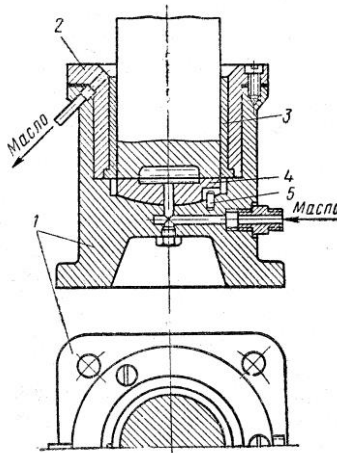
Схема подпятника: 1 – корпус; 2 – кольцо
